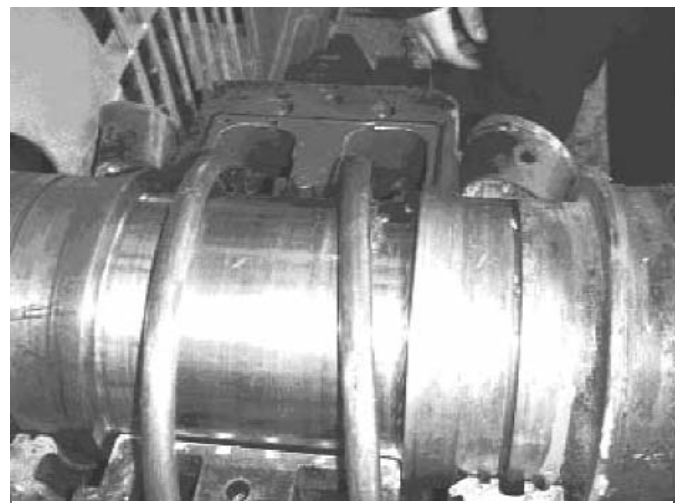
Подшипниковая опора со снятой верхней крышкой
